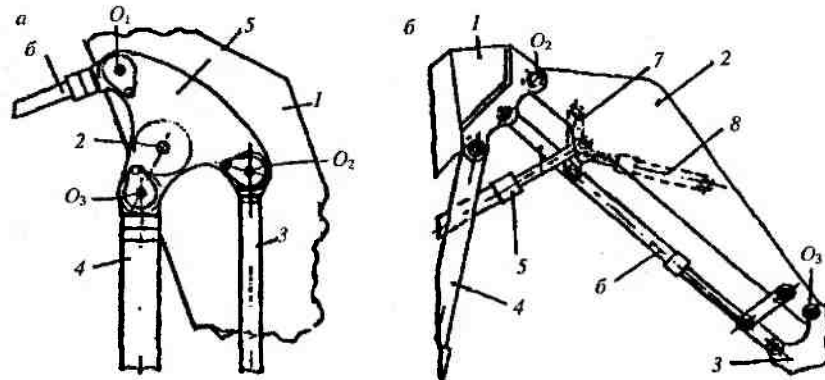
Схемы установки силовых цилиндров гидравлических экскаваторов:
